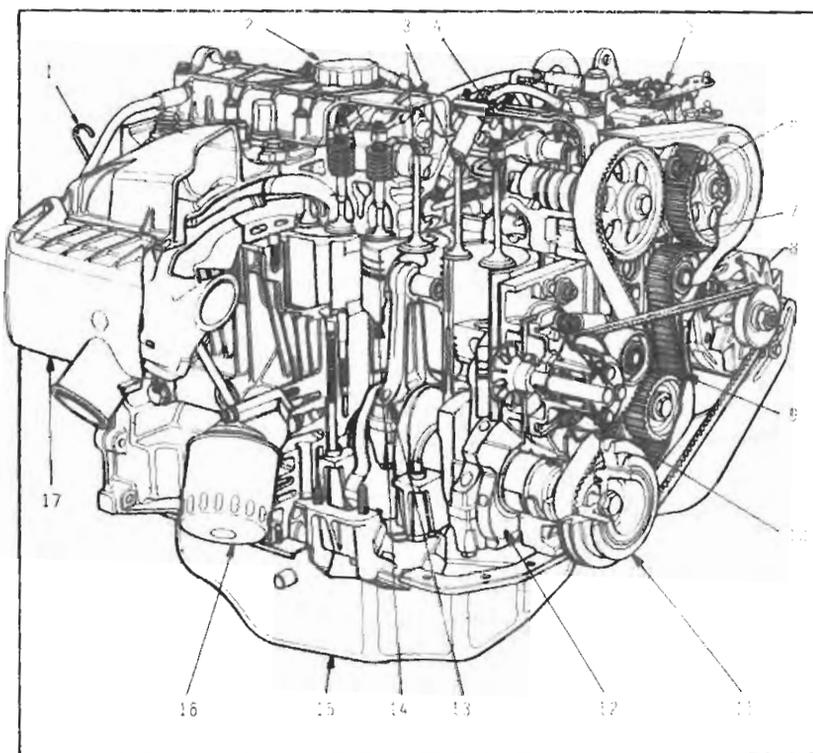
Motor Diesel ligero de 2.063 cc. (RENAULT). 1.- Varilla de nivel de aceite. 2.- Tapón de llenado de aceite. 3.- Válvulas. 4.- Balancín. 5.- Bomba de inyección. 6.- Engranaje de la bomba de inyección. 7.- Engranaje del árbol de levas. 8.- Alternador. 9.- Correa de distribución. 10.- Bomba de agua. 11.- Polea del cigüeñal. 12.- Cigüeñal. 13.- Biela. 14.- Pistón. 15.- Cáster. 16.- Filtro blindado de aceite. 17.- Envoltura del filtro de aire.
